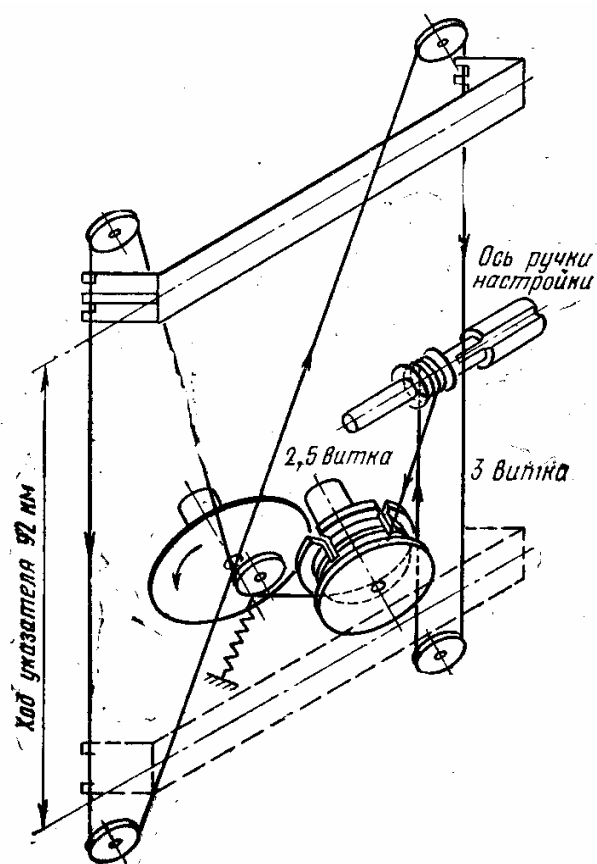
Кинематическая схема верньерного устройства магнитол «Вега-320» и «Томь-305»
